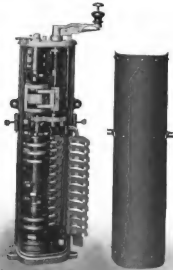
Führerschalter der Zugsteuerung Sprague-General Electric Co.
